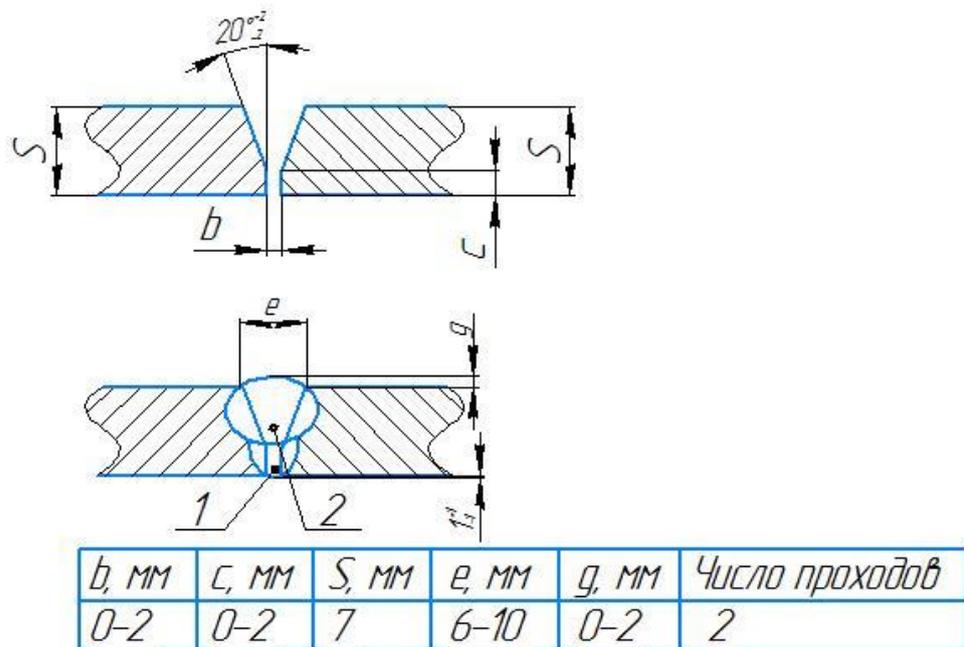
Геометрические размеры разделки кромок и размеры сварного шва по ГОСТ 14771-76.
